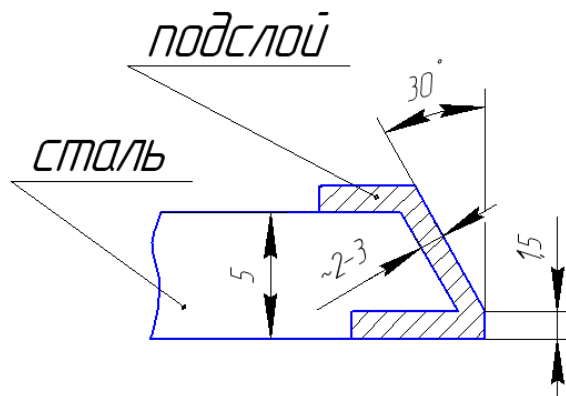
Схема конструктивного элемента из стали 04Х20Н6Г11М2АФБ с обработанным подслоем ЭП-263Ш под сварку
